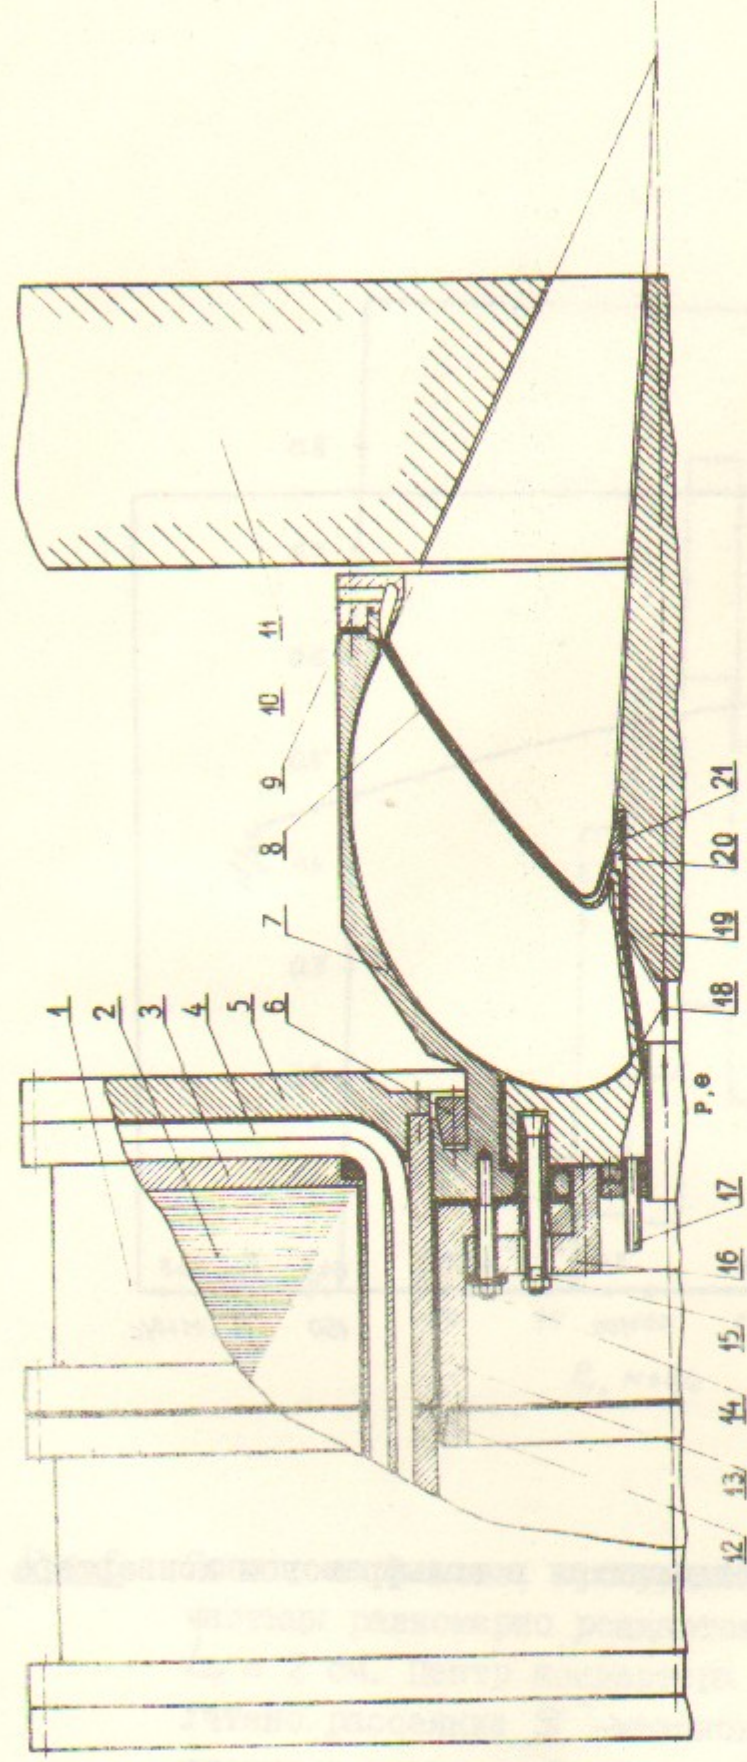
Общий вид линзы. 1 - трансформатор; 2 - тороидальное железо; 3 - объёмный вторичный виток трансформатора; 4 - витки первичной обмотки; 5 - крышка; 6,12 - прижимные кольца цапговых контактов; 7 - профилированная коаксиальная ошиновка; 8 - корпус линзы; 9 - прижимное контактное кольцо; 10,17 - вход и выход системы водяного охлаждения; 11 - свинцовая защита; 13 - коаксиальный токоподвод; 14 - силовые болты, стягивающие ошиновку, 15 - контактные цапги; 16 - упорный фланец для крепления прижимных и отжимных болтов; 18 - мишень; 19 - вольфрамовая пробка; 20 - упорная переходная деталь; 21 - корпус водяного охлаждения.
